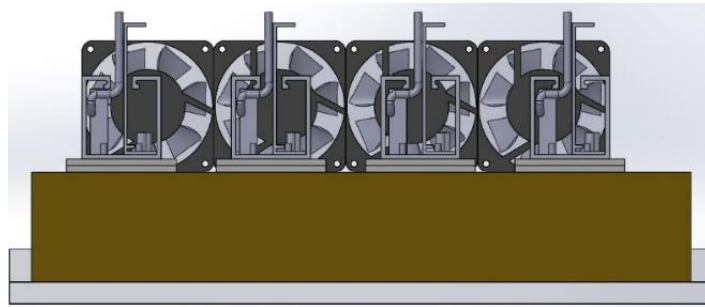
Vista frontal do módulo com a nomenclatura de elementos.
